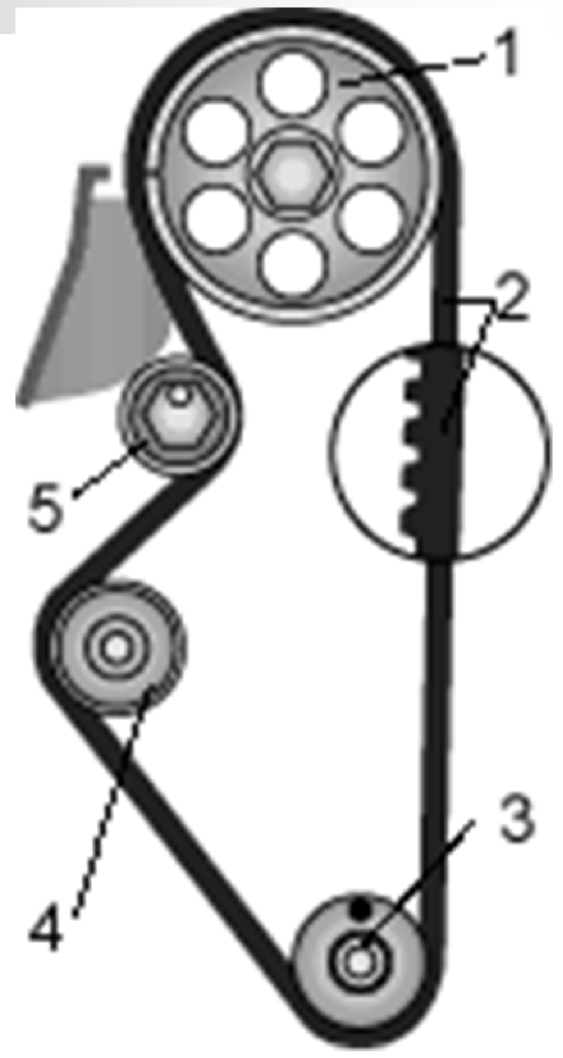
Схема привода распределительного вала двигателя трактора Беларусь 1522.
